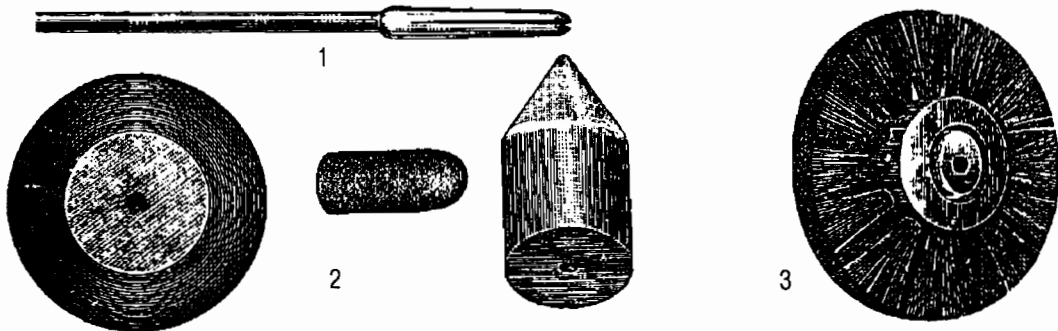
Инструменты для шлифовки: 1 — бумагодержатель; 2 — фильцы; 3 — щетка.
